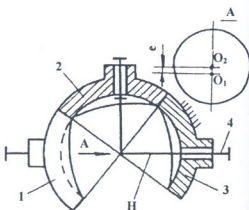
Планетарная передача с эксцентричными коническими колесами
